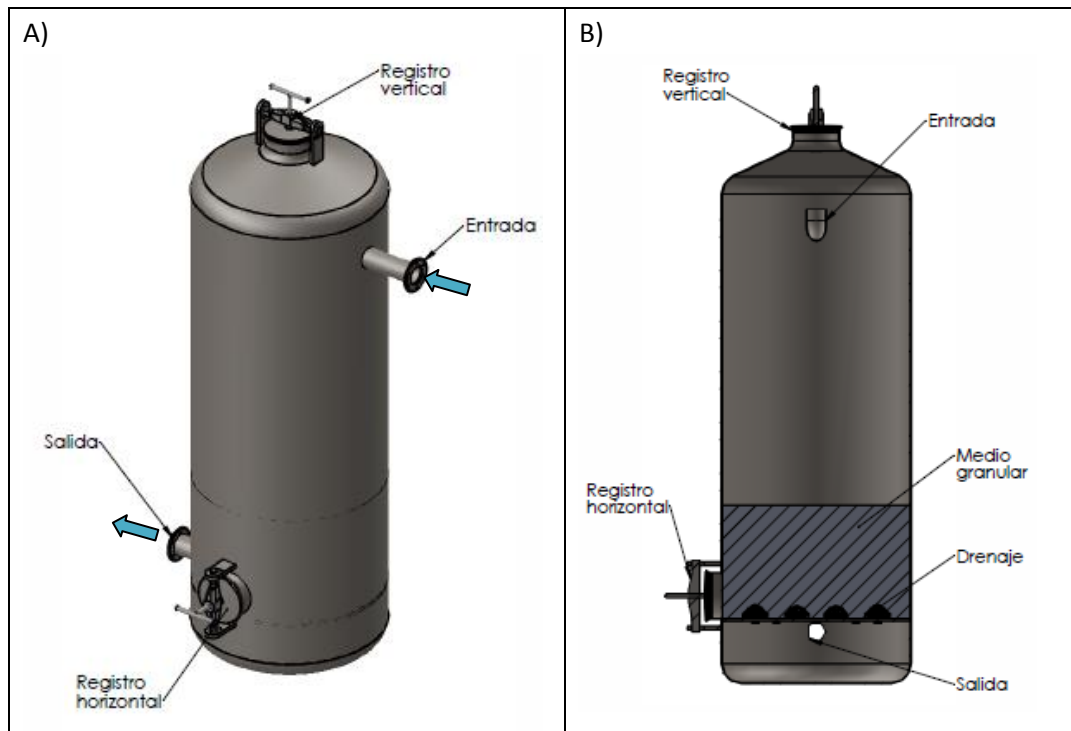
Esquema constructivo de un filtro de matriz granular. A) Vista exterior; B) Corte longitudinal. (Elaboración propia).
